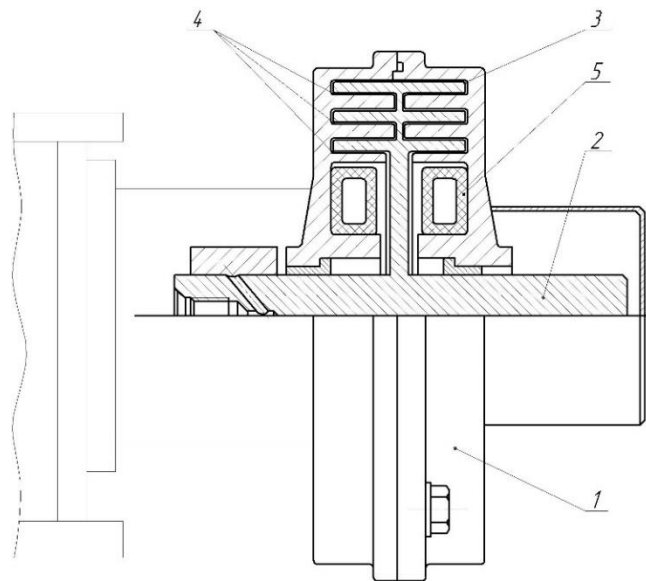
Конструктивна схема роторного гідравлічного гасителя коливачів: 1 - герметичний контейнер, 2 - вал-ротор, 3 - робочі зазори, 4 - робоча рідина, 5 - компенсатор
